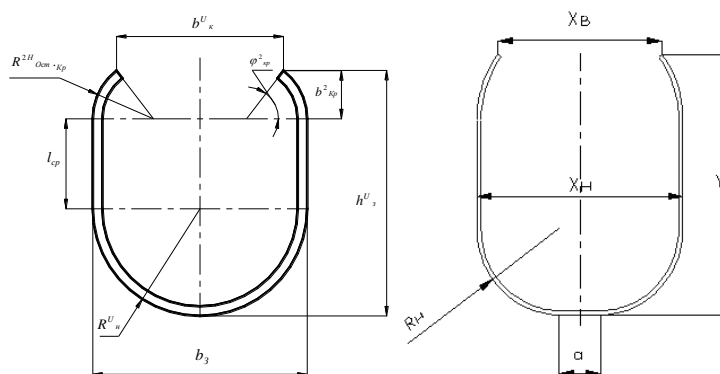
Геометрические размеры U-образного профиля заготовки:
